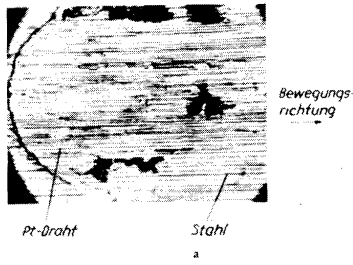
Verschweißung des Thermoelementes Stahl-Platin während des Schweißens
